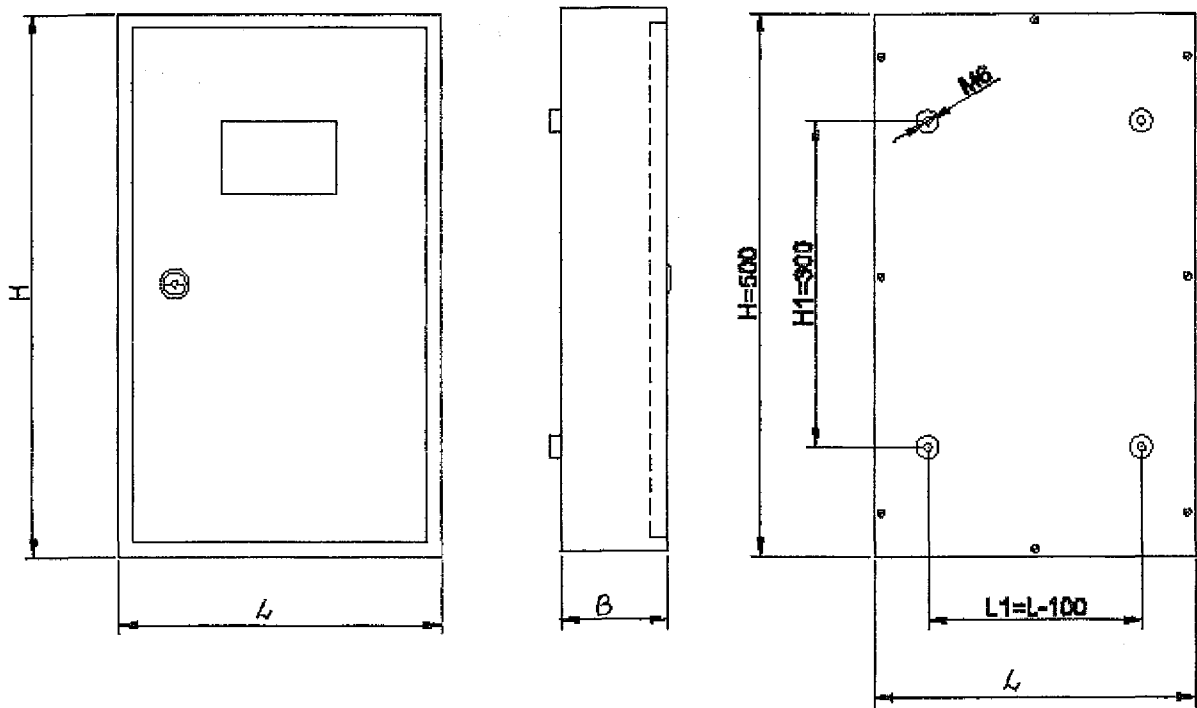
Общий вид, габаритные и установочные размеры щитка ЩКИ
